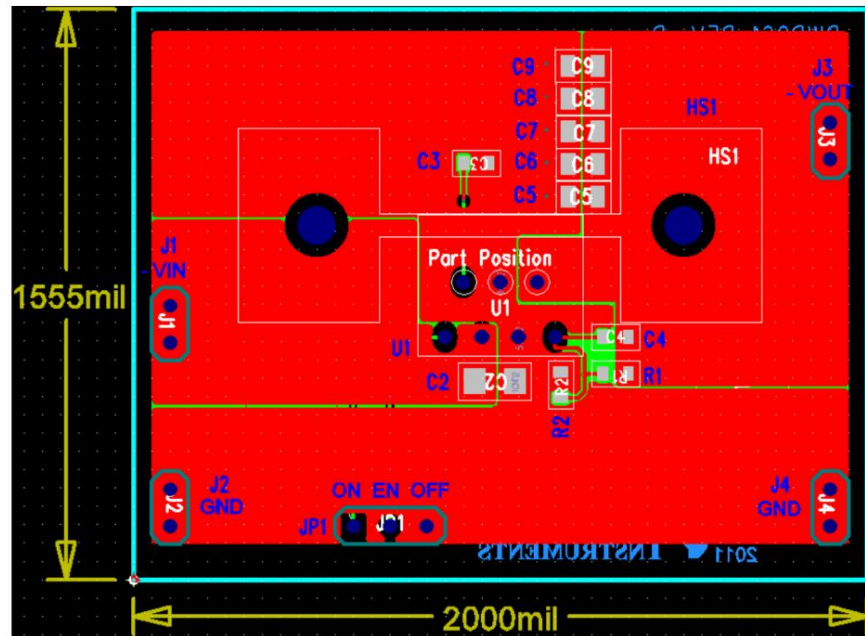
TPS7A33 TO-220 EVM PCB 布局示例:顶层
